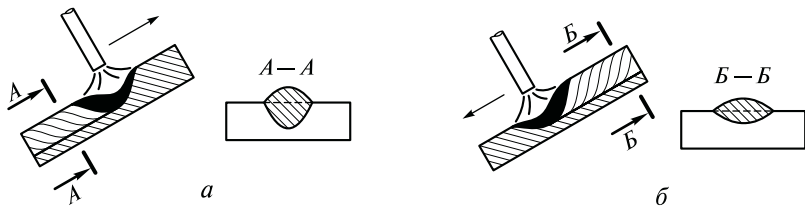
Влияние наклона детали на форму шва при сварке на подъем (а) и на спуск (б)
